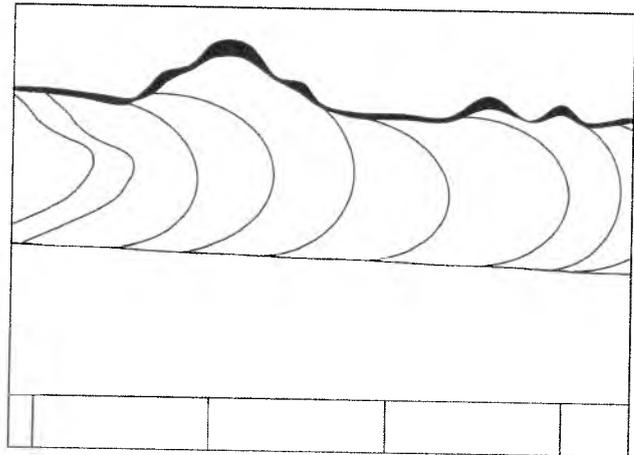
Протяженный подрез в стыковом сварном соединении трубопровода
